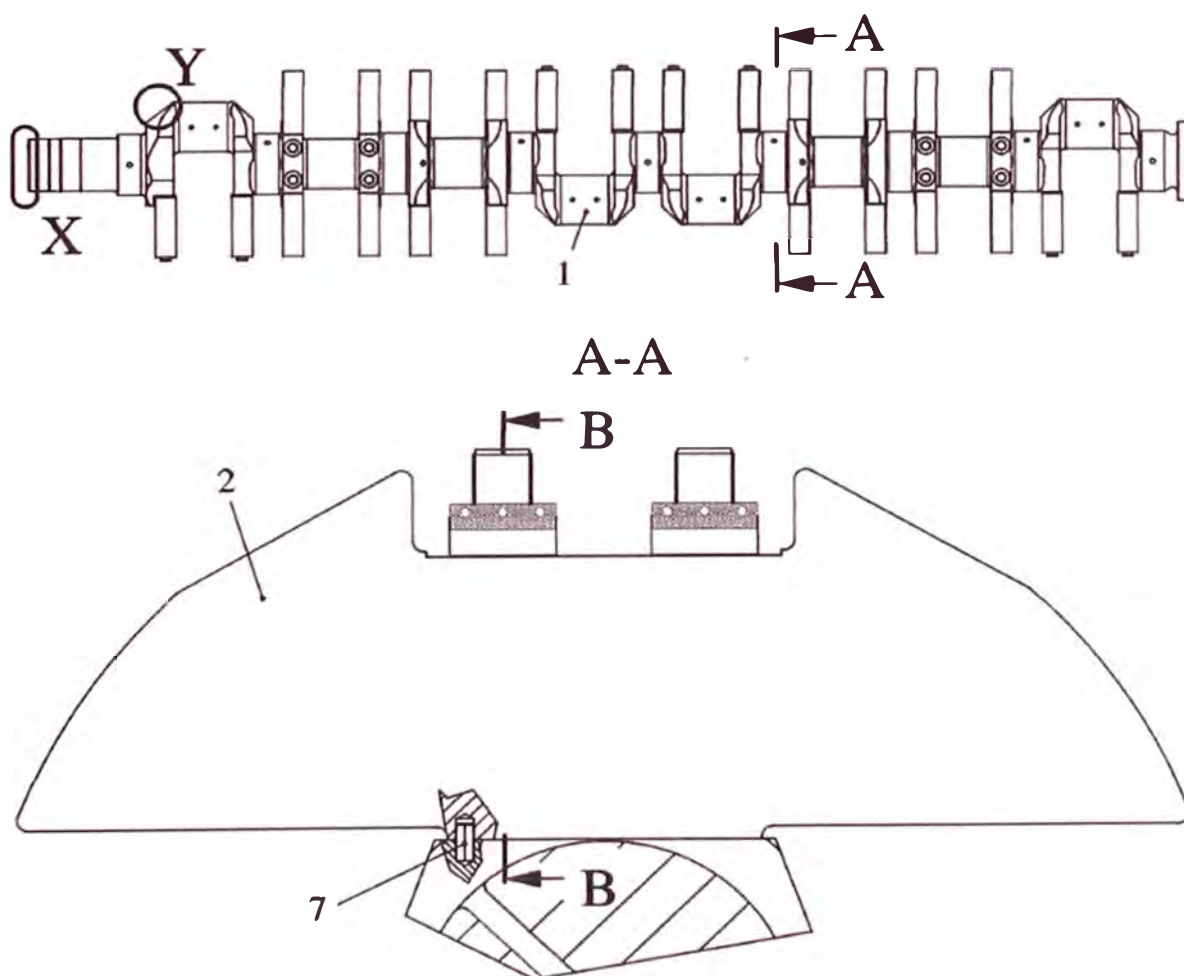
Vistas del cigüeñal, corta A-A vista de contrapesa
